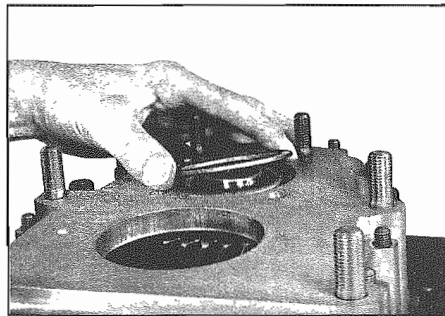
Montaggio di un rasamento di spessore Placing the one shim washer
